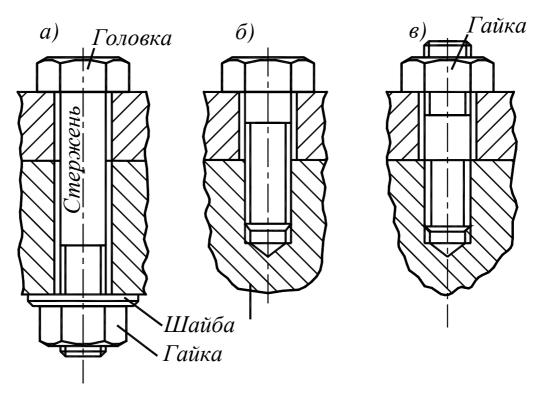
Виды резьбовых соединений: а) болтовое; б) винтовое; в) шпилечное *Болт* представляет собой стержень с резьбой для гайки на одном конце и головкой на другом (рис. 19.1, а).
